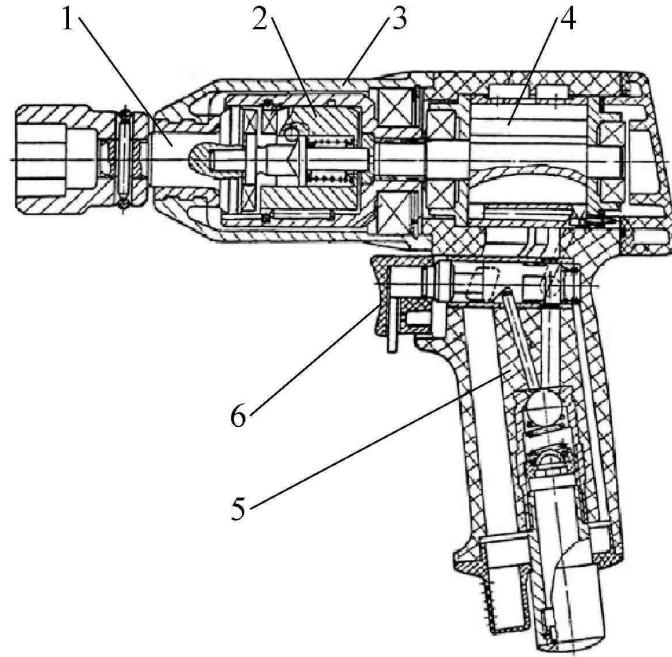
Схема устройства пневматического гайковерта ударного действия: 1 – шпindelь; 2 – ударно-вращательный механизм; 3 – корпус; 4 – пневматический ротационный двигатель; 5 – рукоятка с пусковым устройством и механизмом реверсирования; 6 – кнопка
